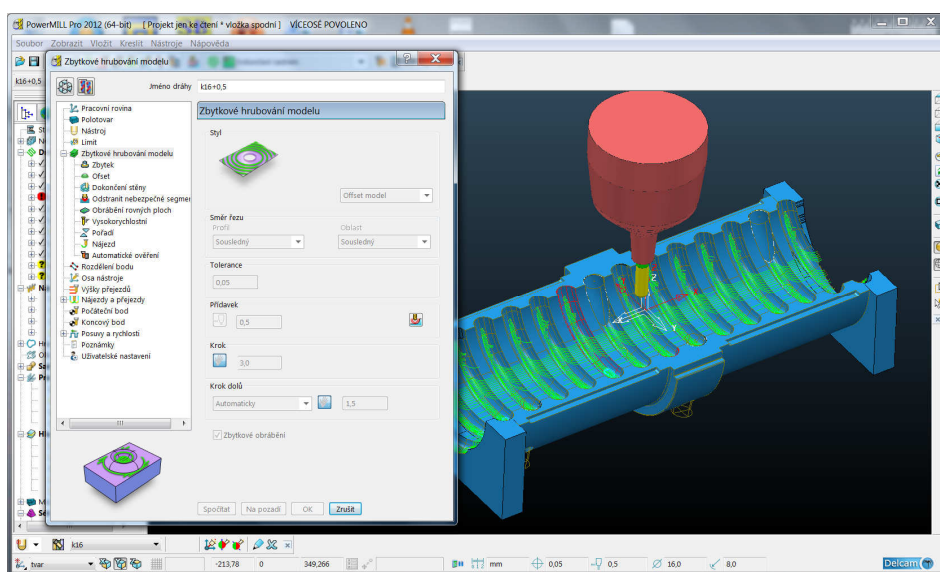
Parametry obrábění pro hrubování závitu Vložky
